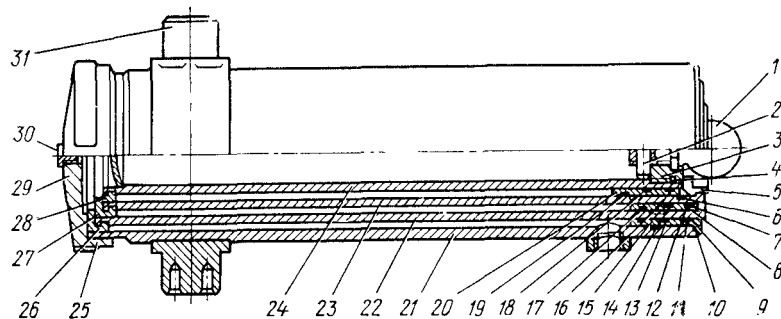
Гидроцилиндр самосвала МАЗ-503
